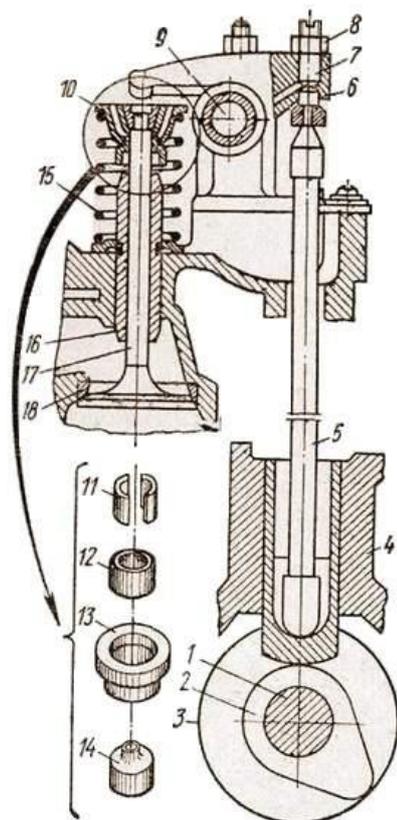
Газораспределительный механизм с верхним расположением клапанов.
